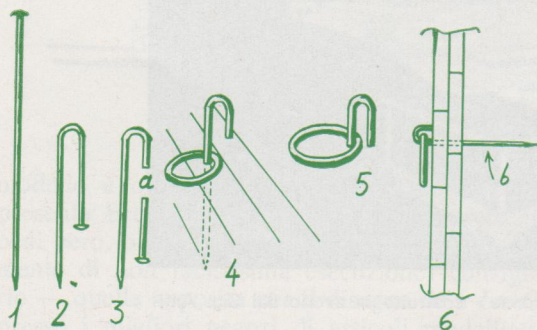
Come fissare facilmente anelli metallici (canestrelli) sui ponti e sulle murate: 1) prendere un chiodino... 2) piegarlo con un paio di pinzette... 3) asportarne la testa col tronchettino... 4) infilarlo al suo posto ed incastrarvi il canestrello... 5) ribatterlo col martello: l'anello è fissato; 6) vista in sezione di un anello nella murata. La parte «b» del chiodo, che spunta oltre la murata, dovrà essere asportata con un tronchettino.
